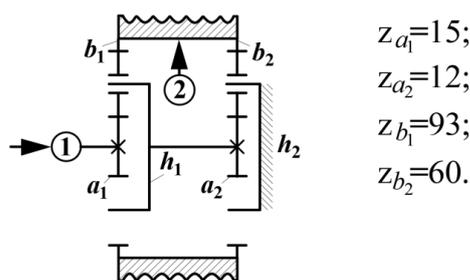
Схема редуктора механизма подъема главной лебедки экскаватора Э-6516
